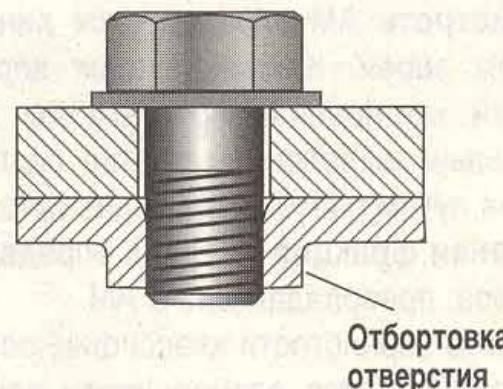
Крепление детали к листовому металлу резьбовыдавливающим болтом.
